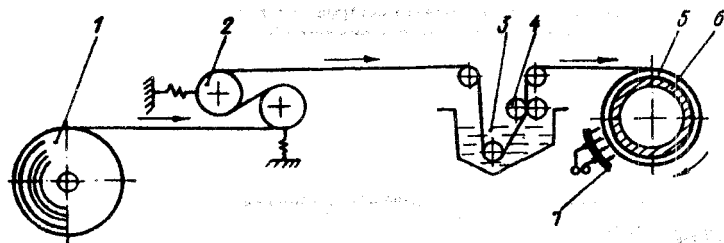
Схема установки для нанесения защитного стеклопластикового покрытия на стальные трубы:
